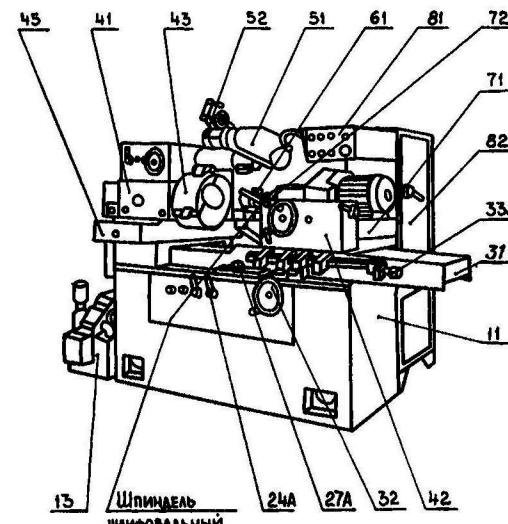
Общий вид станка модели ЗК227А с обозначением узлов
